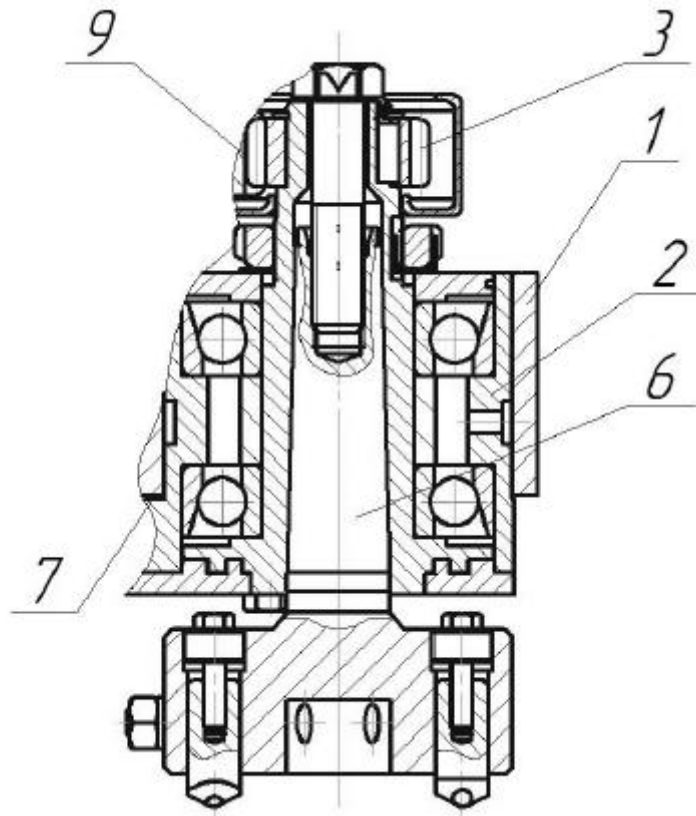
Торцевий багатолезовий інструмент із планетарним рухом формоутворюючих елементів
